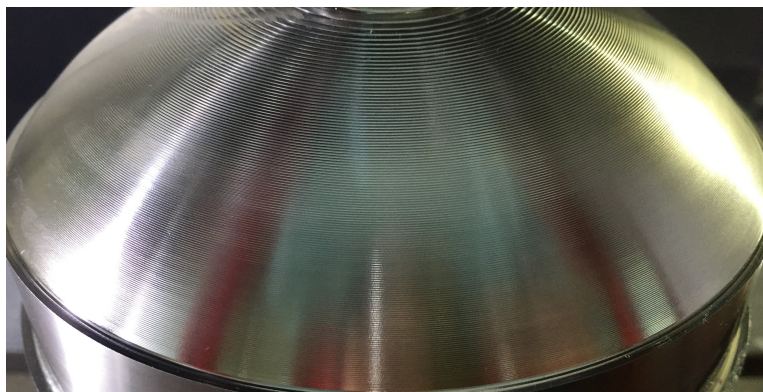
Superfície 3D maquinada pela amostra 1 na dureza 61 HRc.
